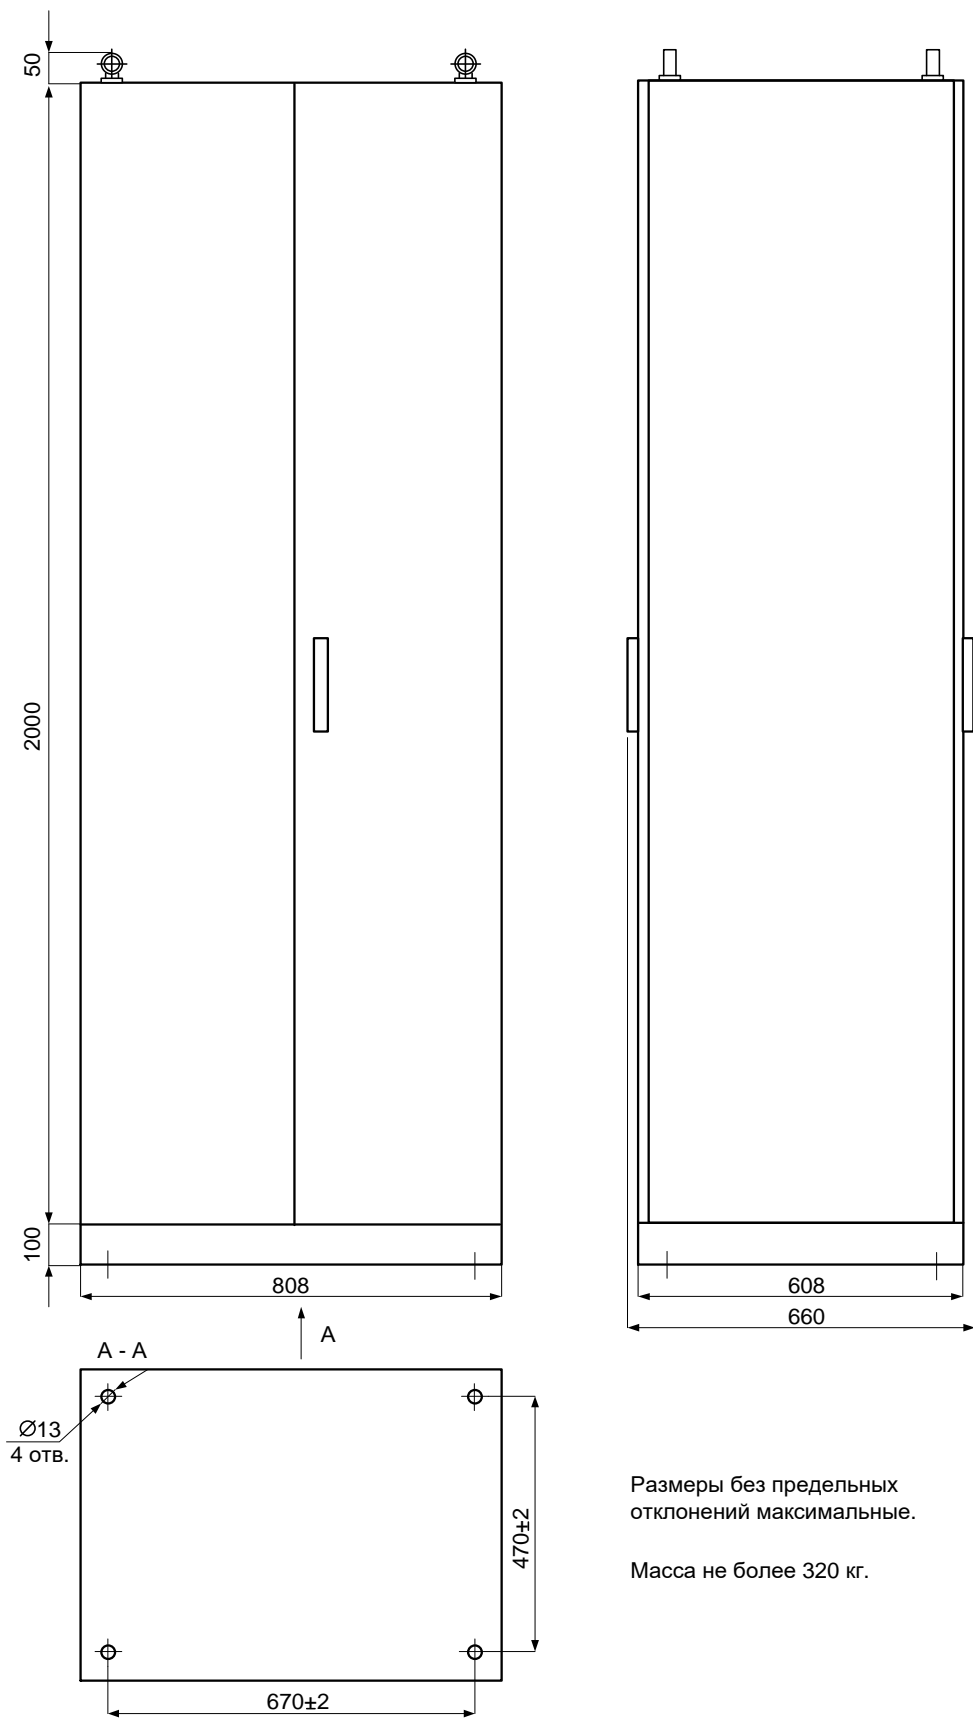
Габаритные, установочные размеры и масса шкафов ШЭ2607 91Х92Х
